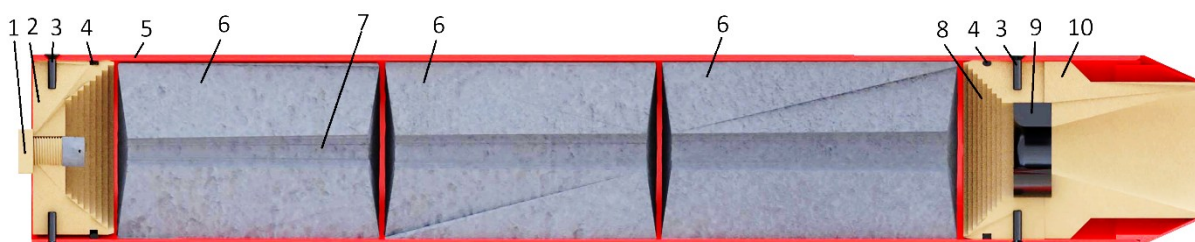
Модель СТРП БПЛА з вкладним зарядом та зіркоподібним каналом: 1 – запальний болт (ініціатор); 2 – передня заглушка; 3 – кріпильчі гвинти; 4 – ущільнюючі кільця; 5 – корпус; 6 – заряд твердого палива; 7 – комбінований торцево-циліндричний канал ; 8 – задня заглушка; 9 – графітова вставка в критичний переріз; 10 – сопловий блок. (розроблено автором у SolidWorks 2021)
